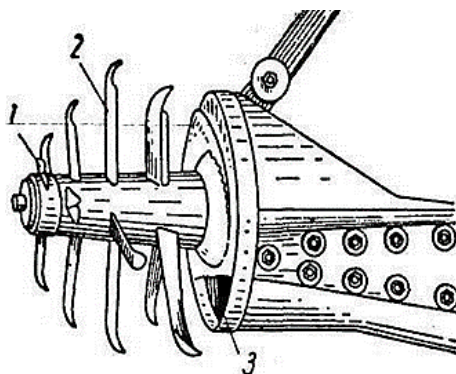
Разрыхлитель с винтовой фрезой: 1 – вал; 2 – лопатки; 3 – отверстие
